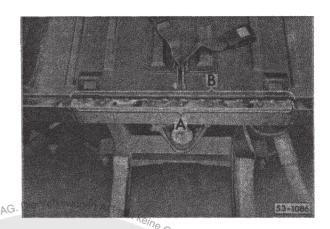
Querträger Deckblech einpassen und einschweißen
